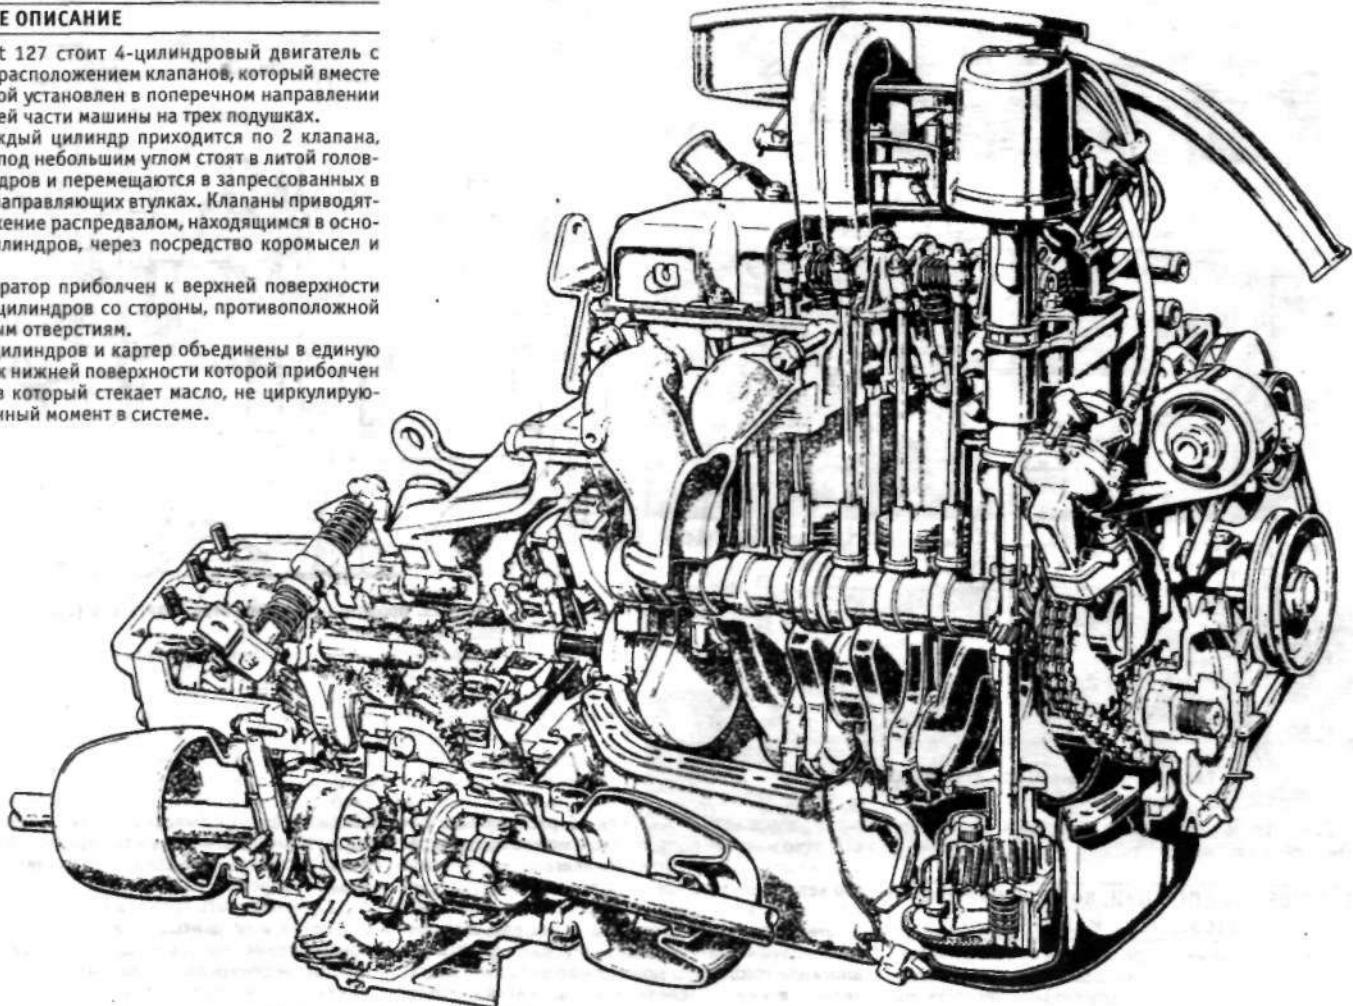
Двигатель 903 см³ и коробка передач (вид в разрезе).
